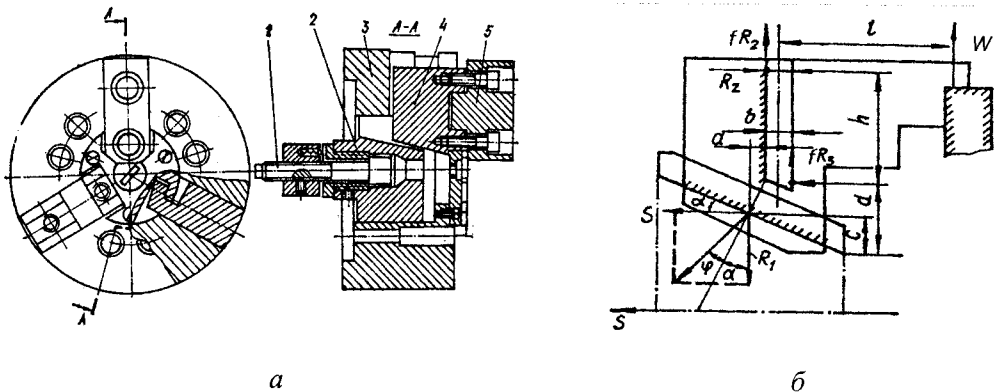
Клиновий кулачковий патрон: а – конструкція; б – розрахункова схема для визначення сил у необертвовому патроні
